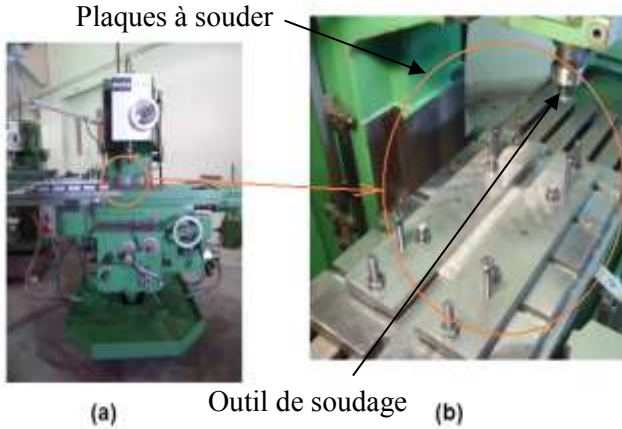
(a) Fraiseuse utilisée pour le procédé FSW (b) système de bridage des plaques à souder
